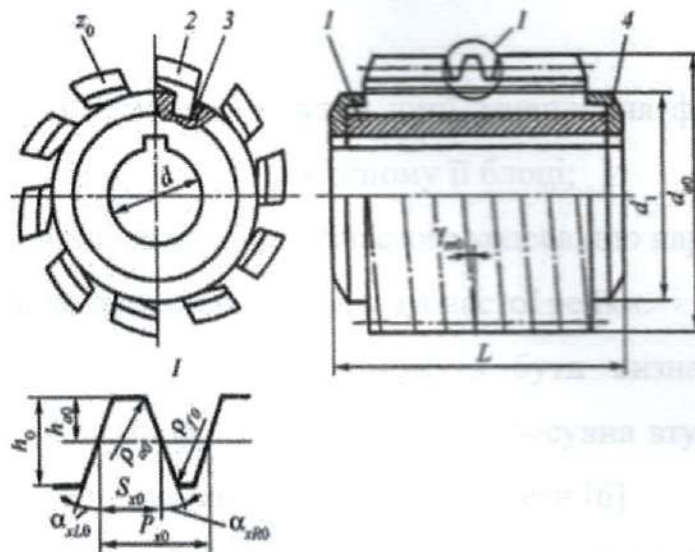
Збірна черв'ячна фреза з поворотними рейками конструкції ВНДІ інструменту
